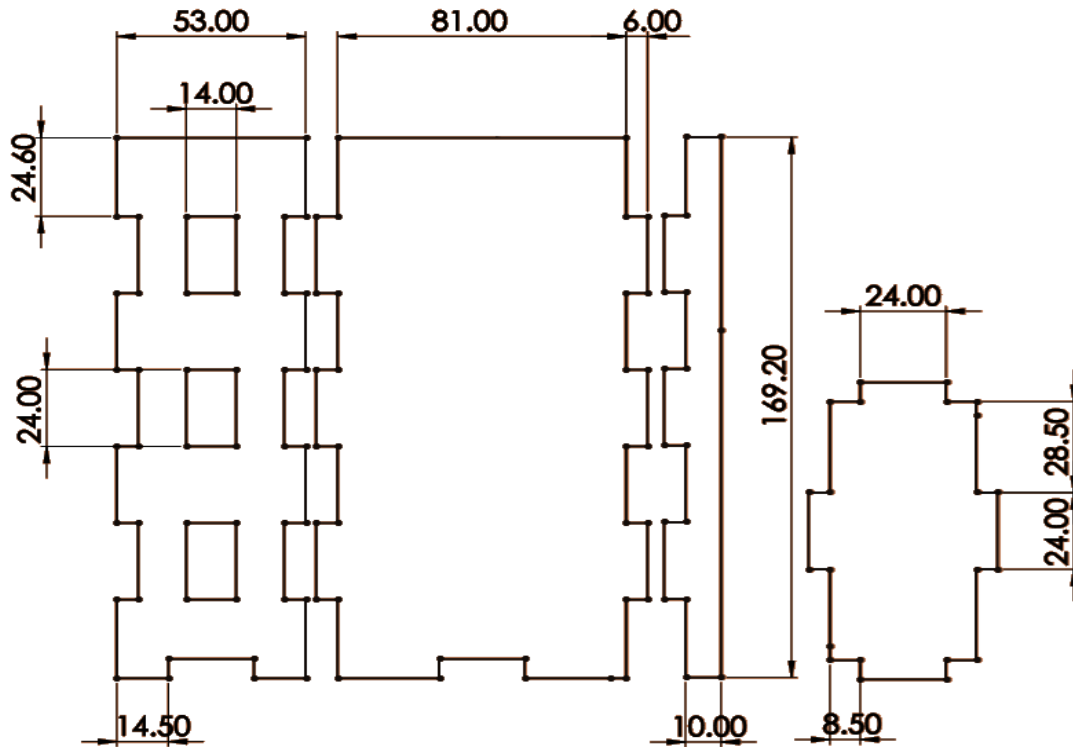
Planos del diseño CAD de los aplicadores utilizados para su manufactura en una cortadora láser.
